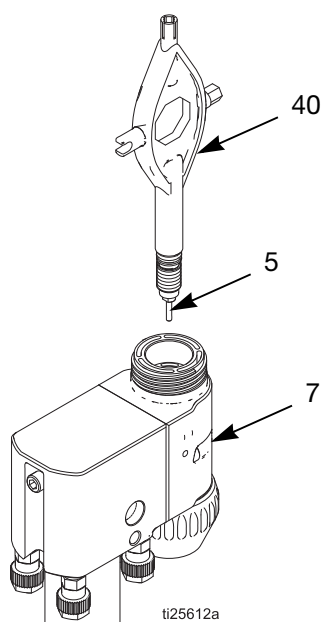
Desmontaje de la varilla de empaquetadura de fluido
